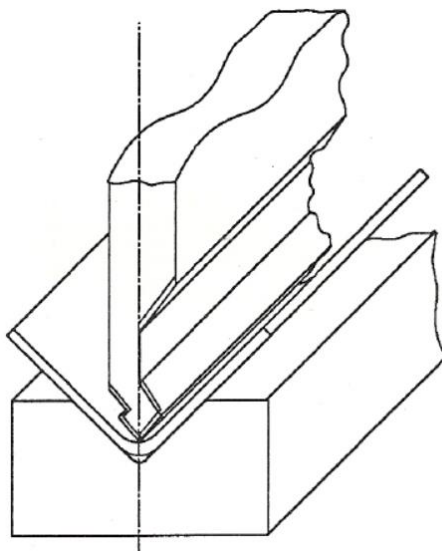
Quinagem a fundo - Contacto entre a chapa e as faces das ferramentas (Bessa Pacheco, 1992)
